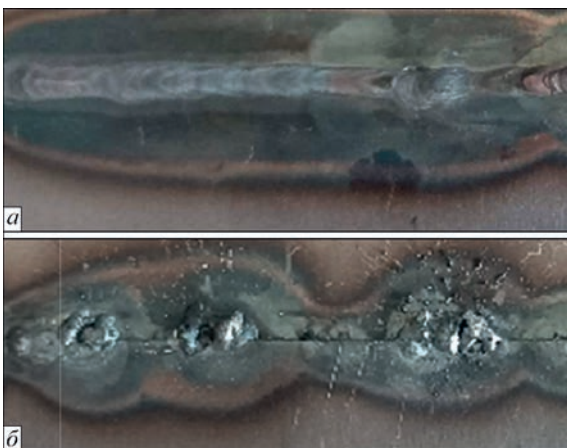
Зразок зварного шва: а – ділянка без дефекту; б – ділянка з дефектом
